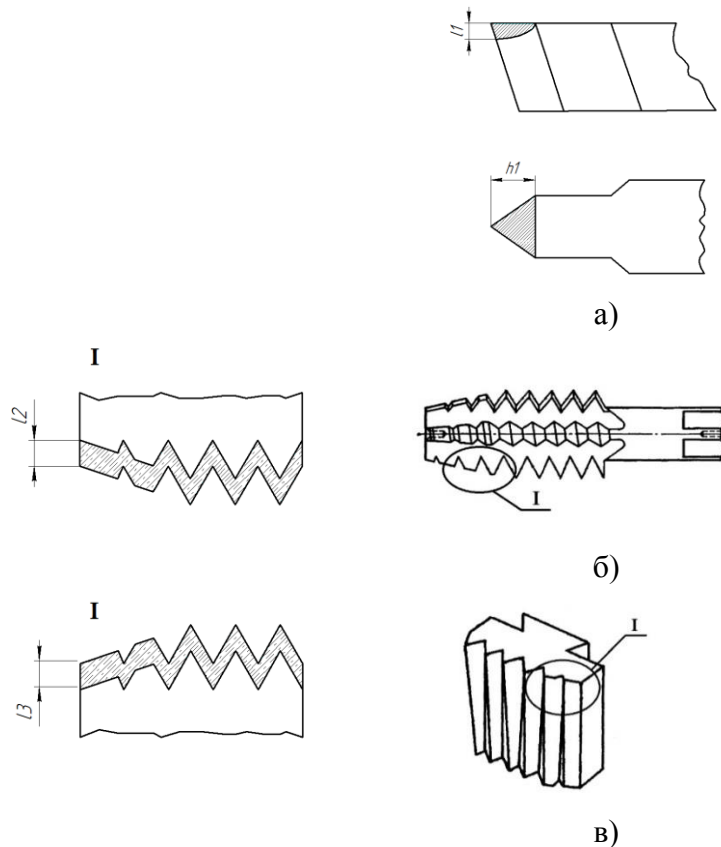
Схема расположения модифицированной зоны при плазменной обработке резьбонарезного инструмента: а – резцов; б – метчиков; в – гребенок
